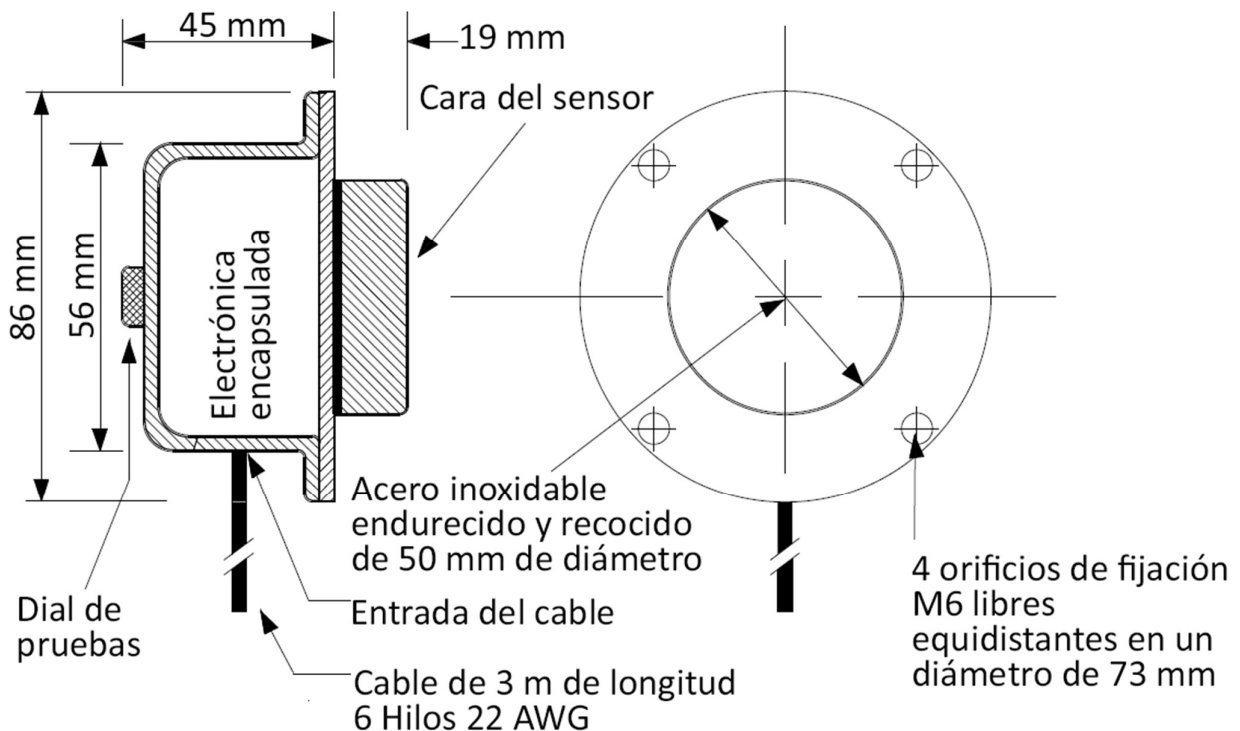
Dimensiones mecánicas del TouchSwitch™
